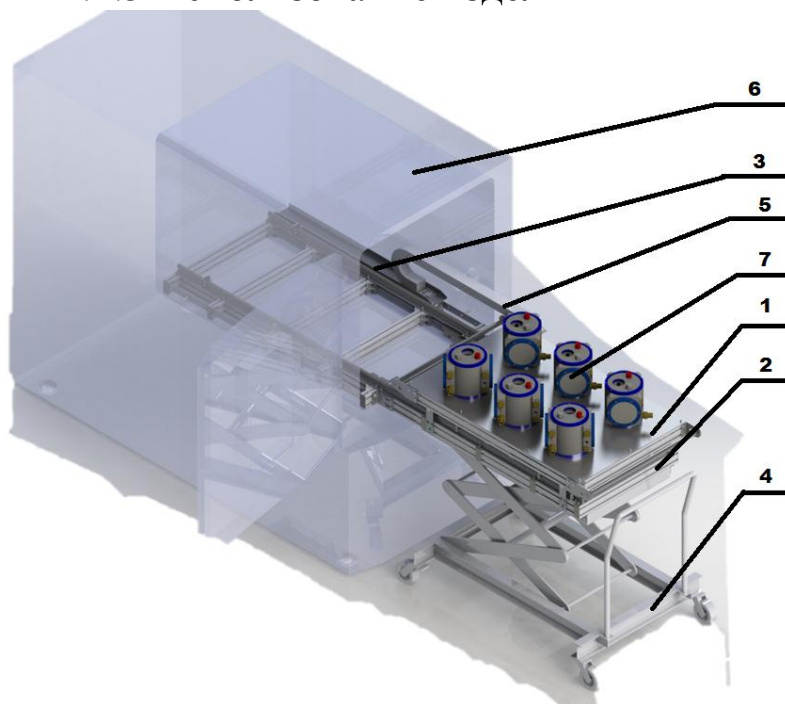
Вид изделия в сборе.(1- сдвижная платформа; 2- направляющая площадка;3- опорная площадка; 4- тележка LMFD-80; 5-гибкий кабель-канал; 6-климатическая камера; 7-БУР.)
